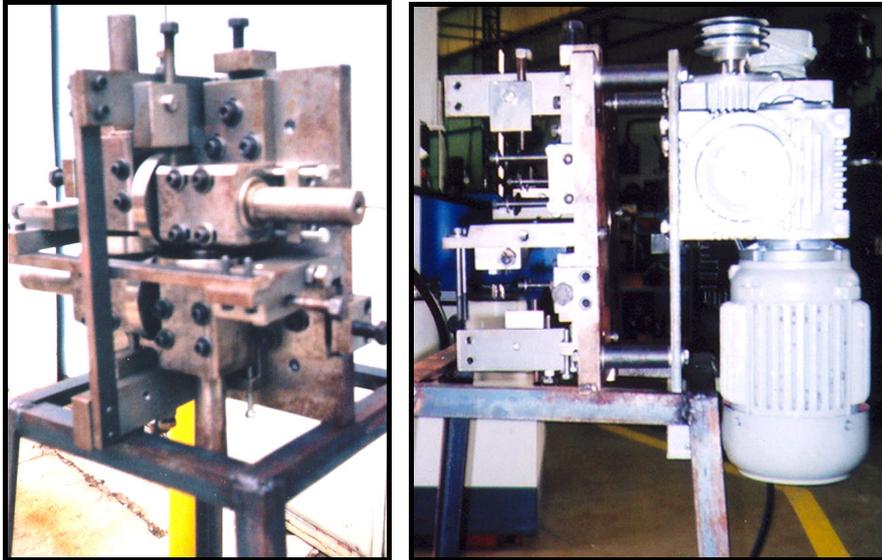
Vistas do laminador após montagem e fixação em um suporte de cantoneiras.
